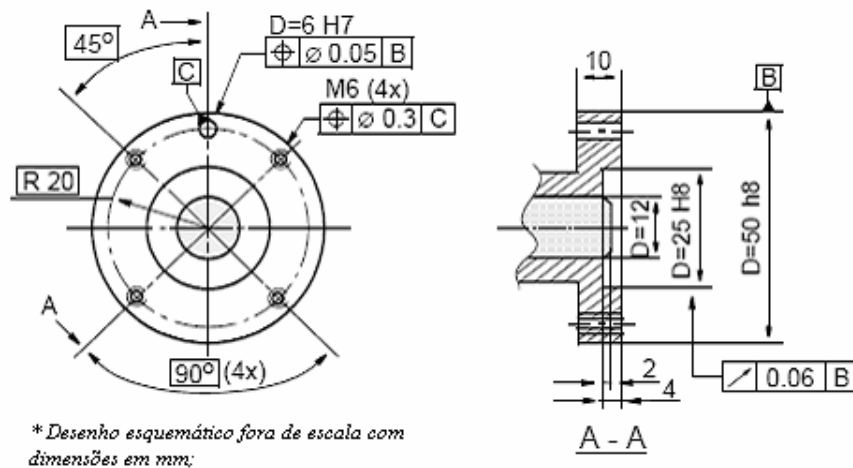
Desenho esquemático do flange de fixação do robô IRB 1400 [ABB, 1993].
